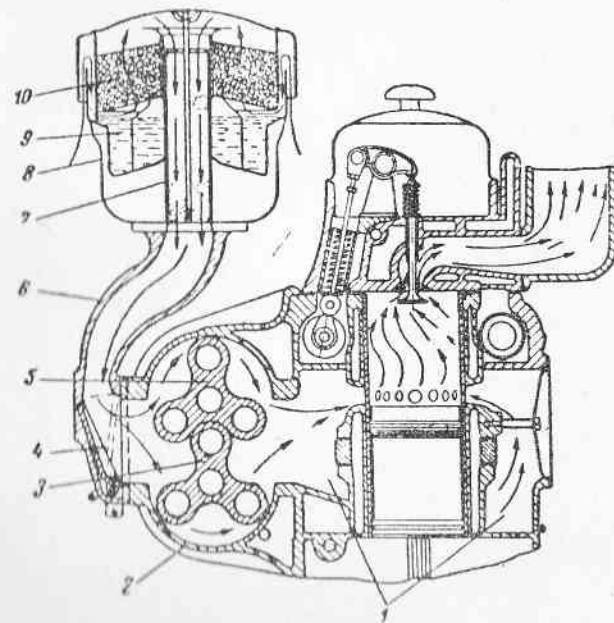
Схема системы питания двигателя YA3-204 воздухом:
